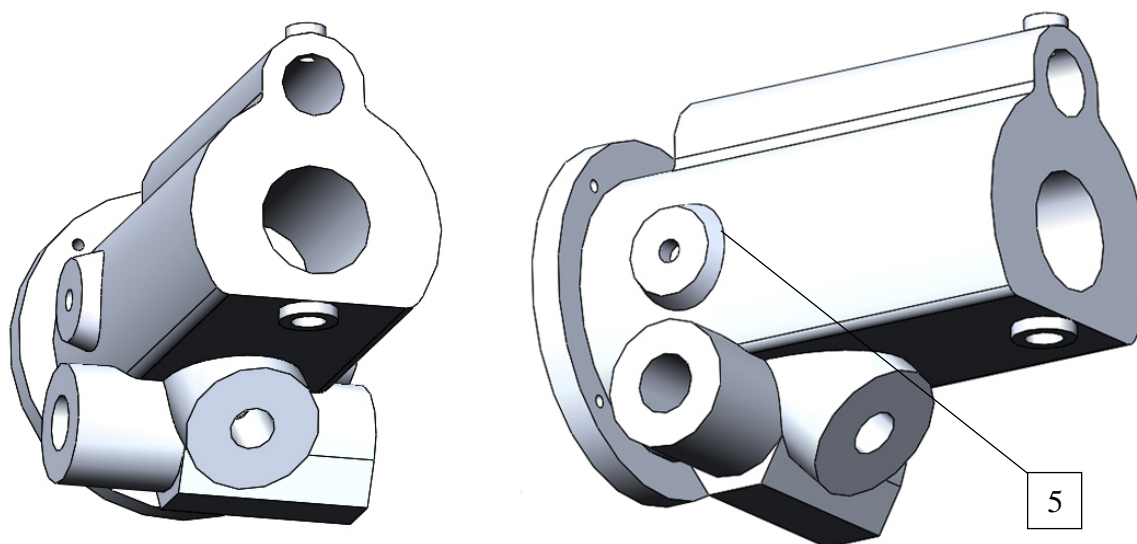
Модель корпуса автомата управления турбины с противодавлением (вид слева)
